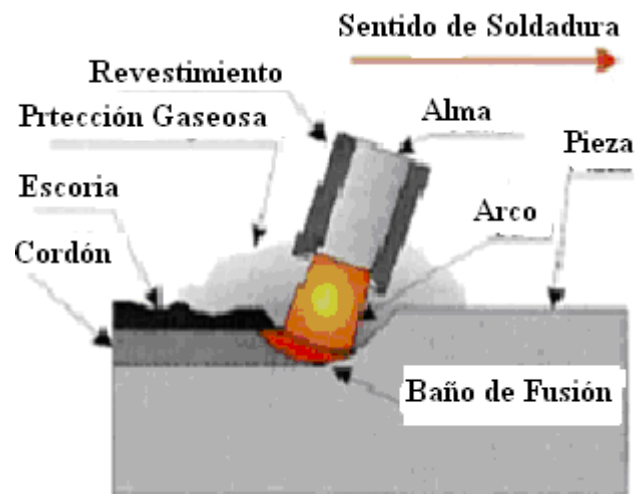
Elementos presentes en la soldadura por arco eléctrico
